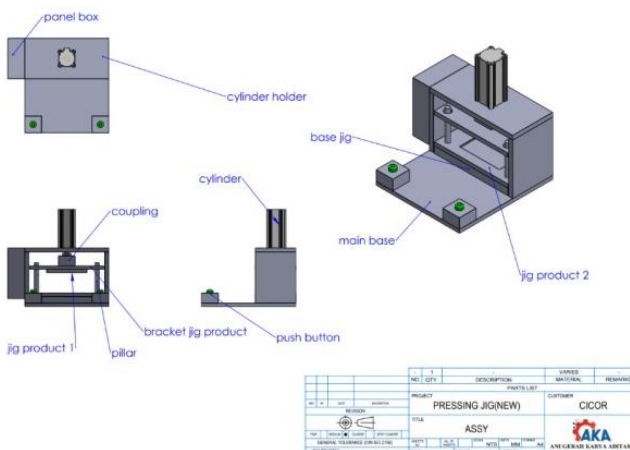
Tampak Isometri Manual Pressing Jig Diseji P702
